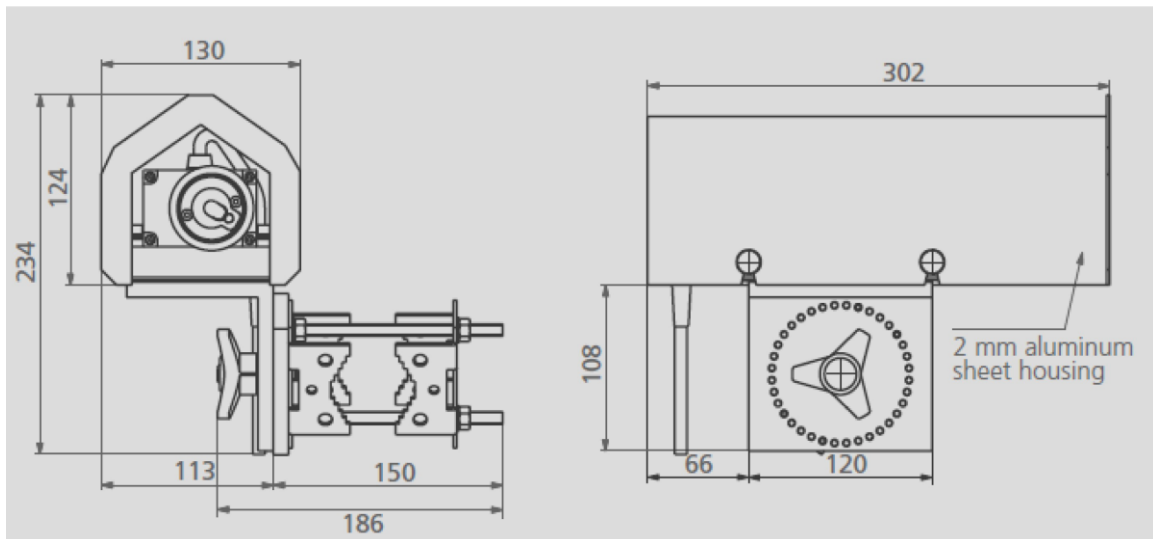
SHM 31 Maße, Technische Zeichnung
